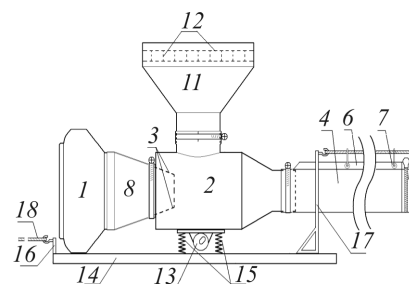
Пневмотранспортная установка для уборки снега с крыши [1]
